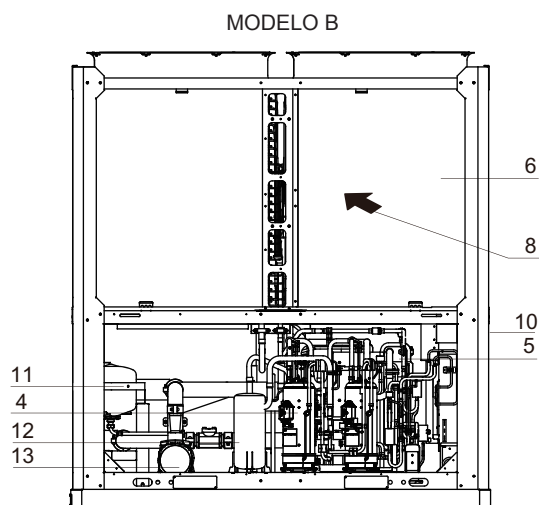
Partes principais do KEM-180 DRS5 KH
